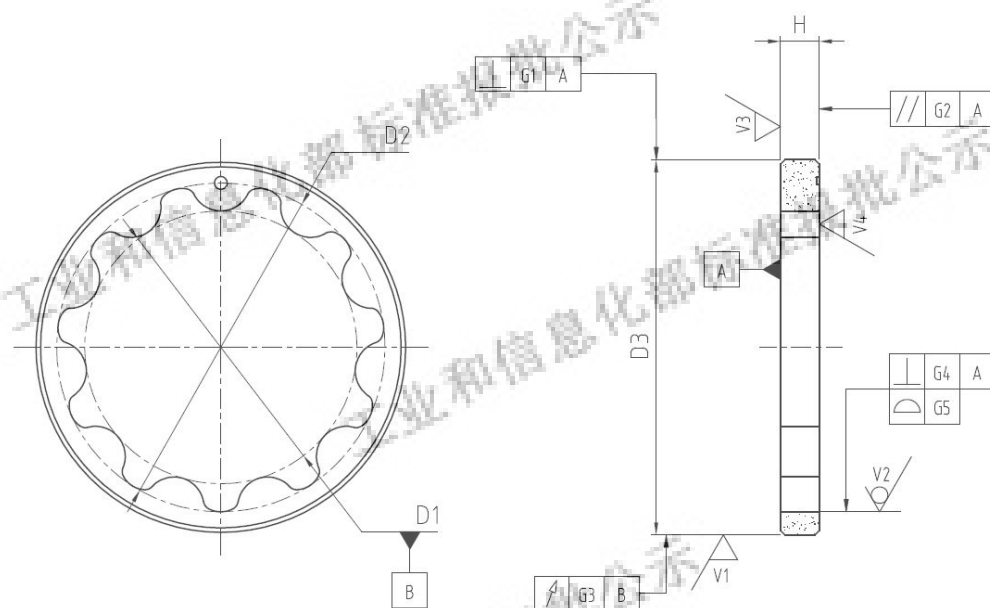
机油泵外转子尺寸、几何公差及表面粗糙度标注示意图
